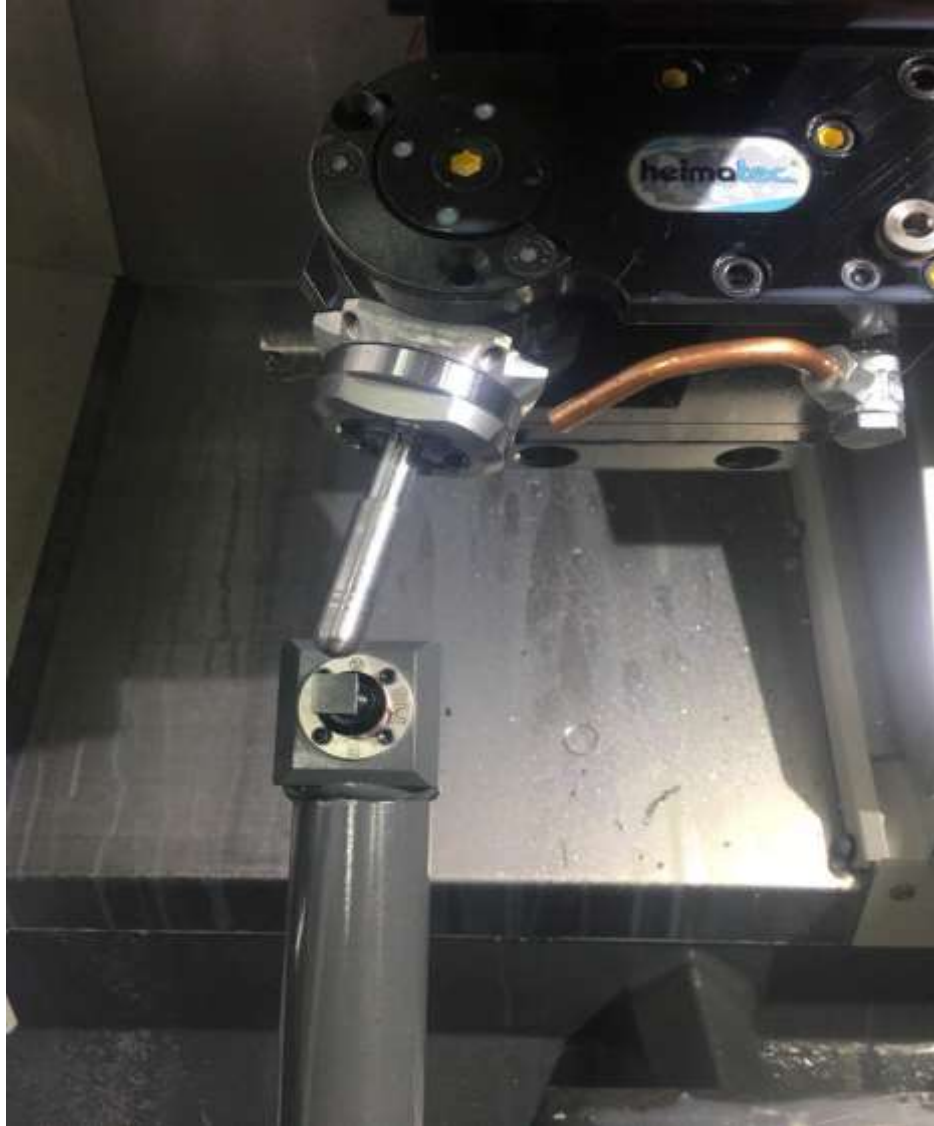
Метод визначення точки позиціювання різального інструмента завдяки інструменту «Напівсфера»
